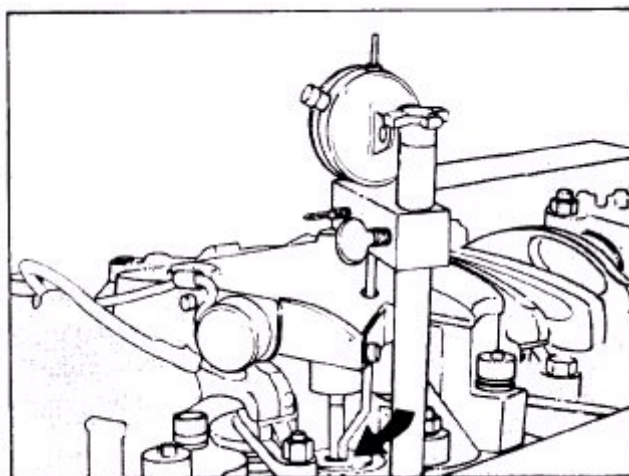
(OM1061L). Установка циферблатного индикатора – удлинитель, касающийся толкателя.
